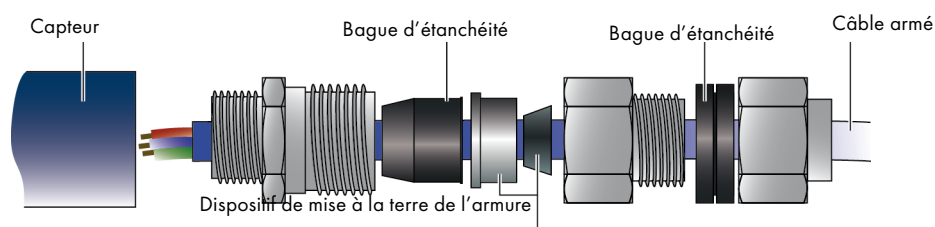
exemple de presse-étoupe double-compression pour serrage sur câble armé.
